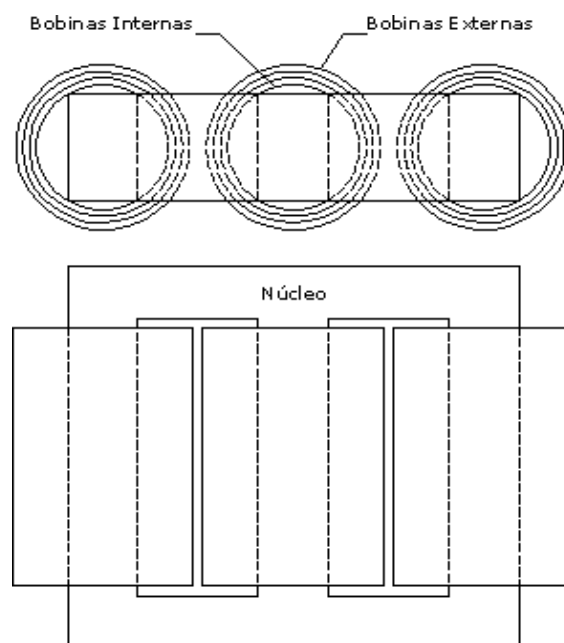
Esquema de construcción de un núcleo a columnas de tres fases.
